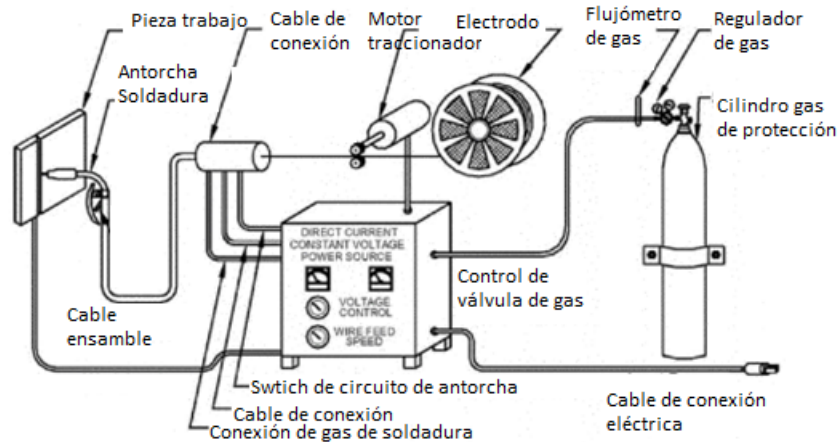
Componentes básicos de equipo de soldadura (Galvery & Marlow, 2006).
